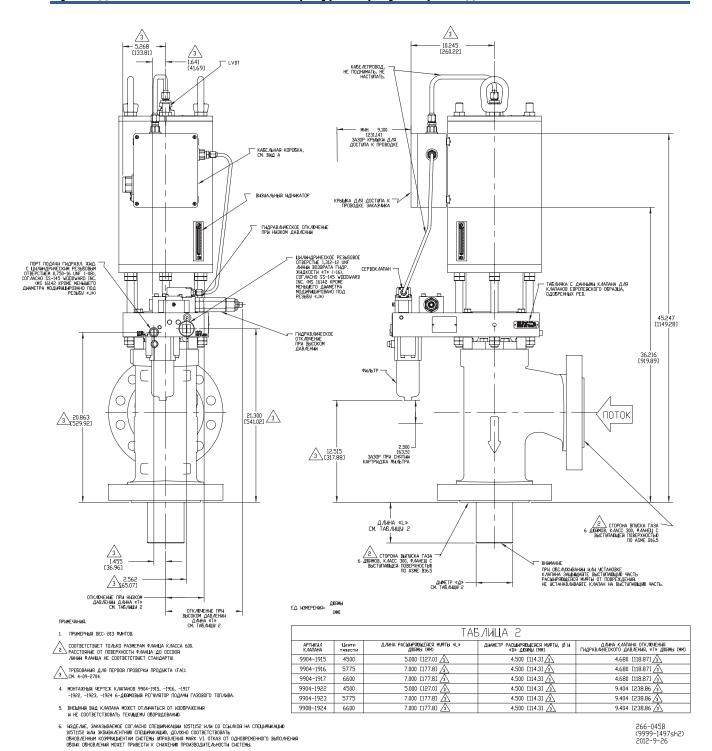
Габаритный чертеж регулятора SonicFlo (6 дюймов, класс 600)
